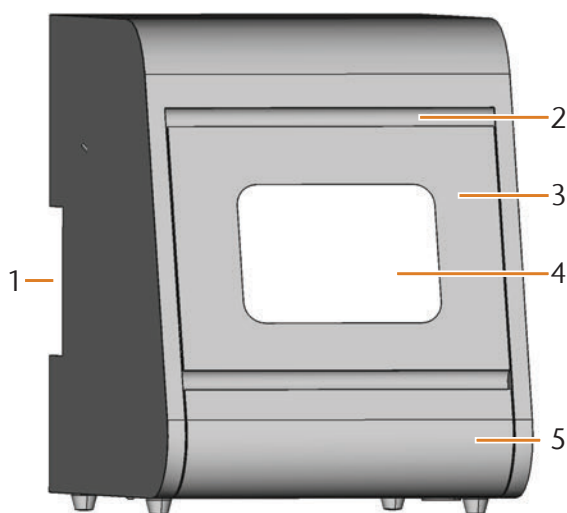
VUE DE FACE DE LA MACHINE N4 IMPRESSION
